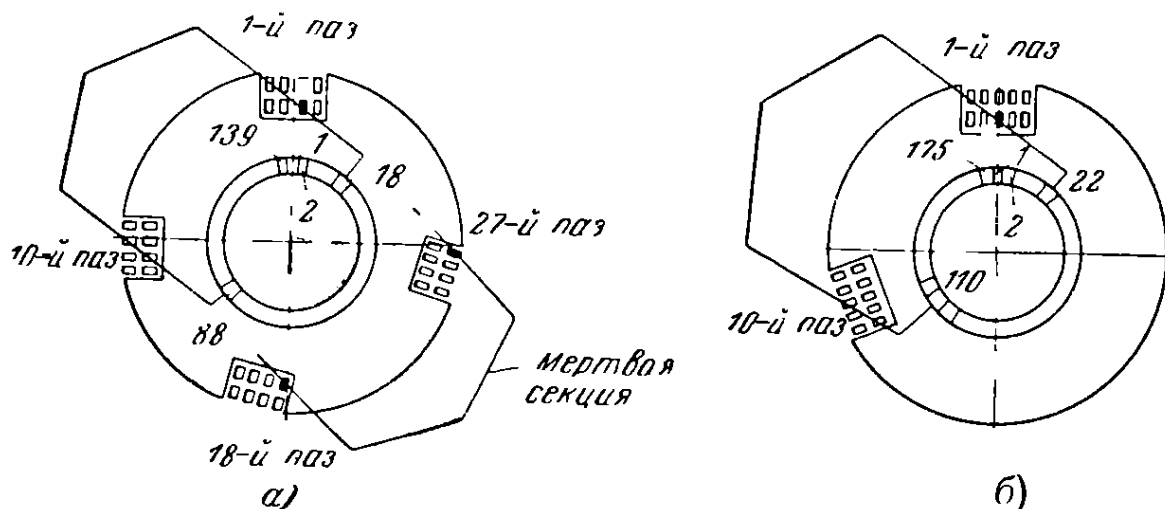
Примеры выполненной разметки якорей двигателей с волновой обмоткой.
